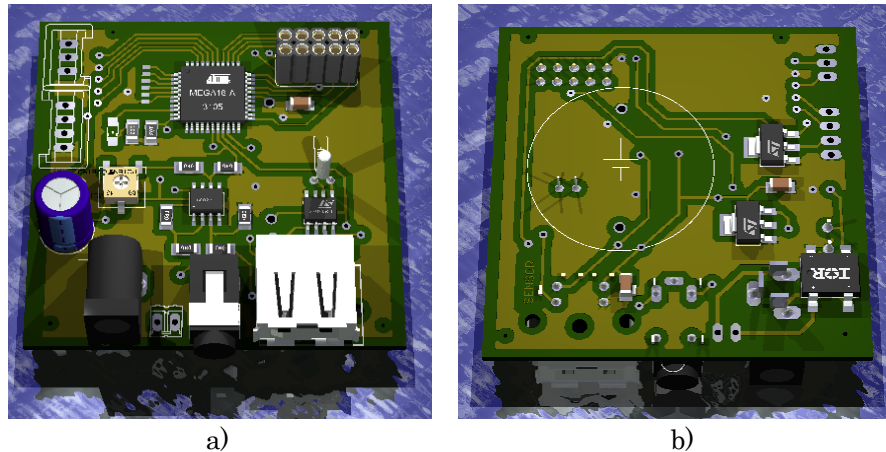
, PCB de la tarjeta de control en 3D. a) Top. b) Bottom.
